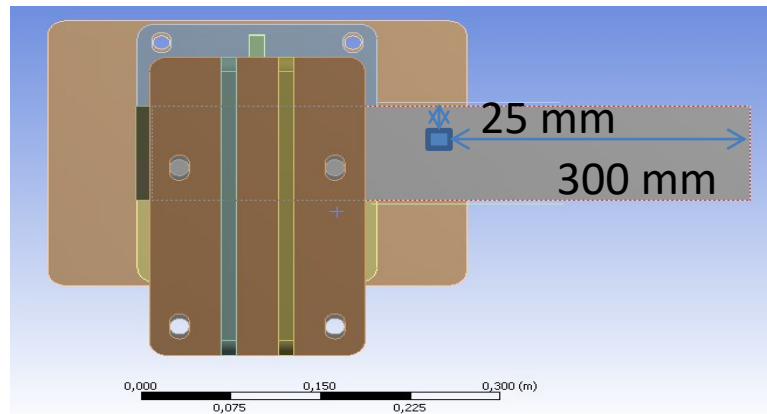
Position de la jauge sur la poutre installée sur le gabarit (vue de dessus)
